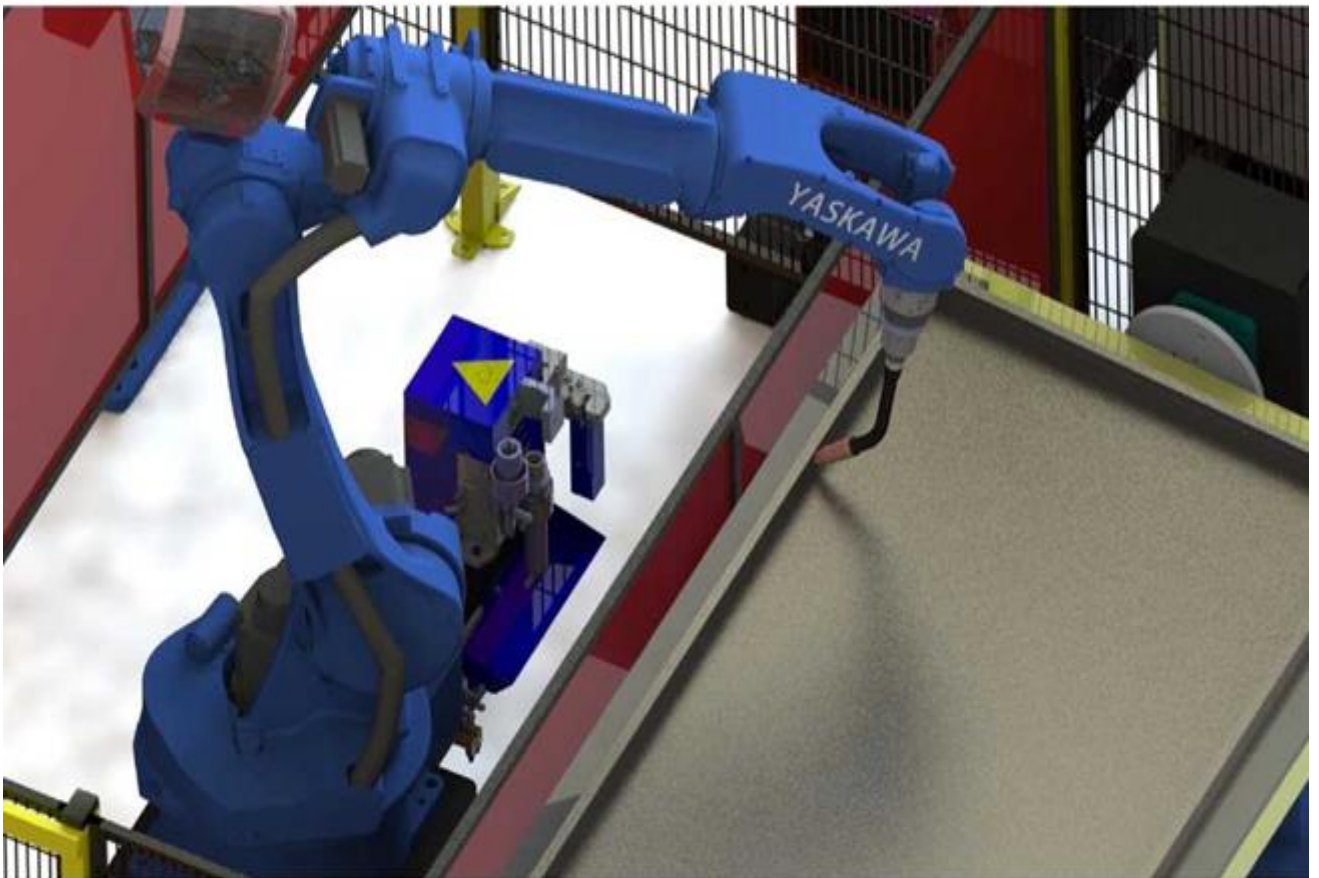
Схематичне зображення робочої зони роботизованого комплексу, зварювання дверного полотна
